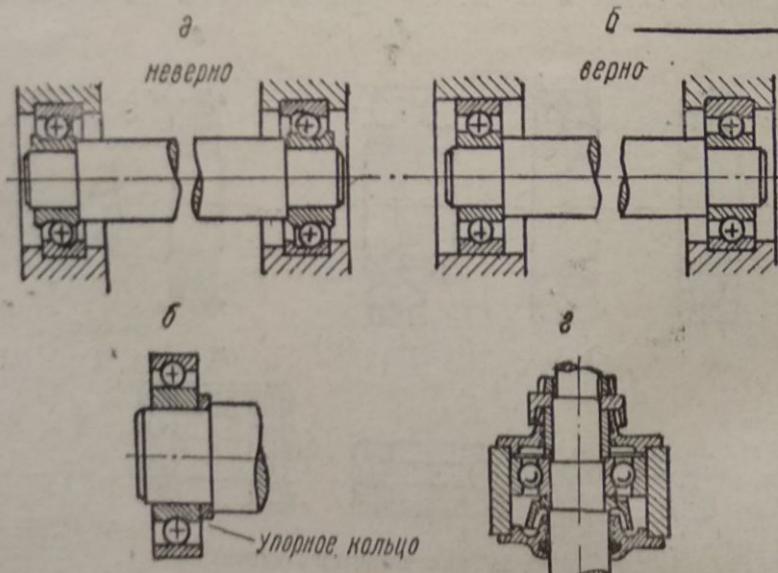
Закрепление подшипников и смазка вертикального шпинделя:
